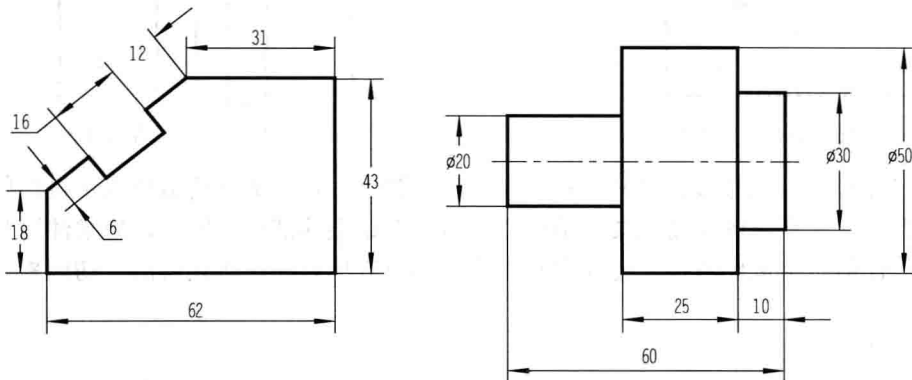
非水平方向线性尺寸的尺寸数字标注
